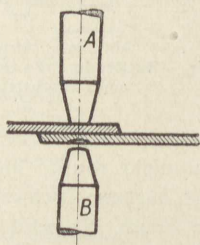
Marke beim Schweißen mit Punktschweißung.
